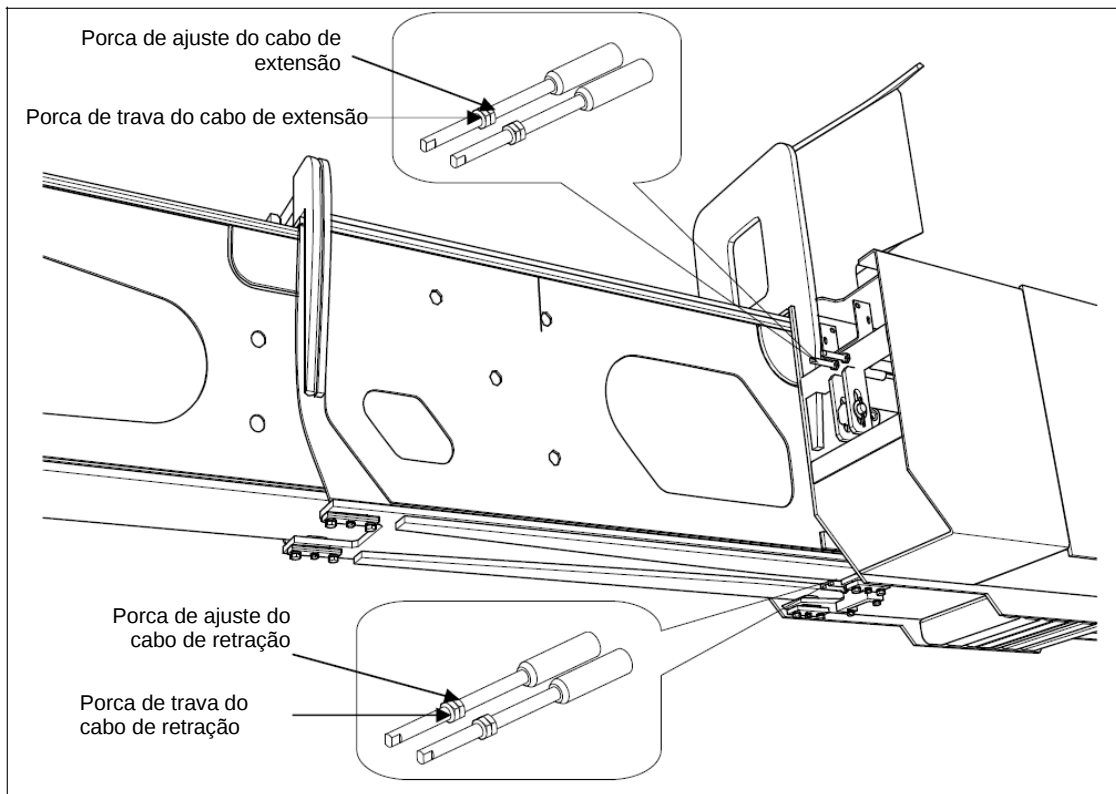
Ajuste do cabo de retração da viga deslizante
